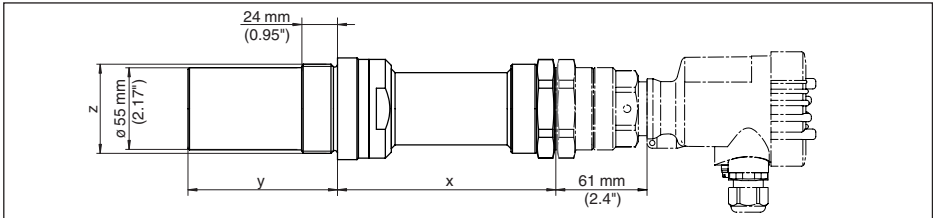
Montageadapter mit Tubus (optional) für frontbündigen Einbau, für VEGAMIP 61 mit innenliegender Hornantenne, Gewindeausführung G1½ mit PTFE-Abdeckung (auch mit 1½ NPT-Gewinde)
